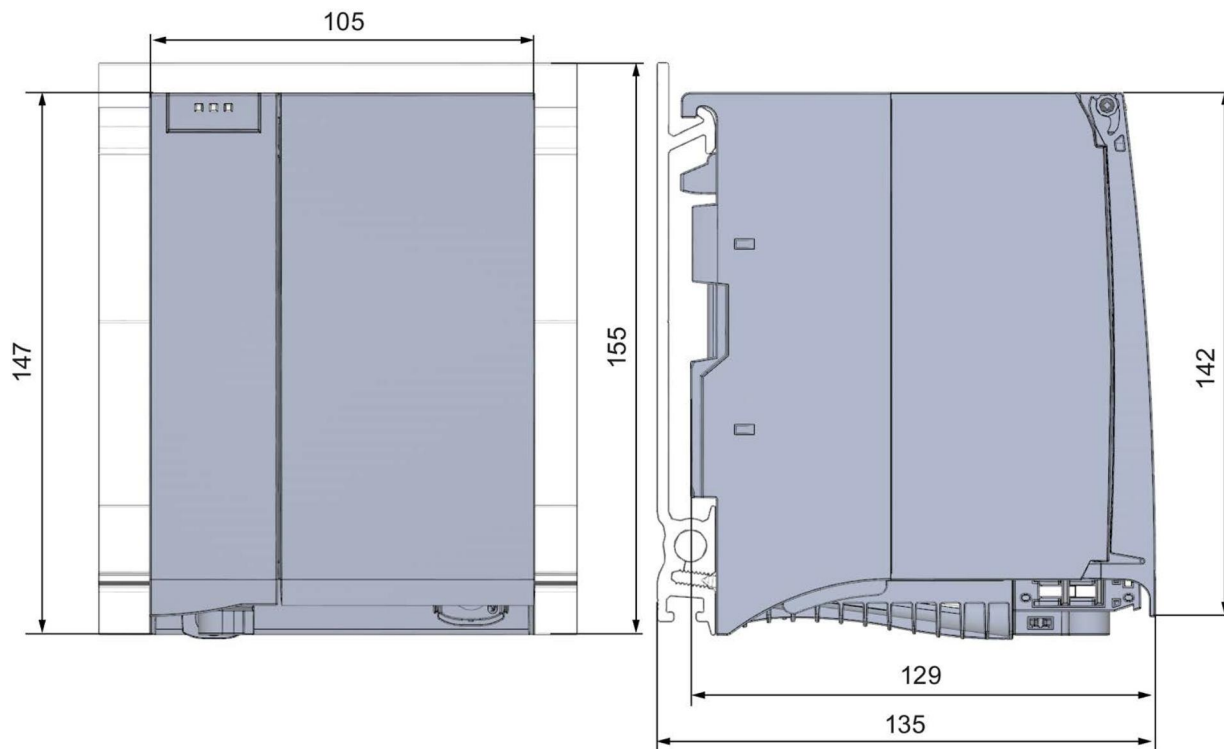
Габаритный чертеж PS 60W 24/48/60VDC HF
